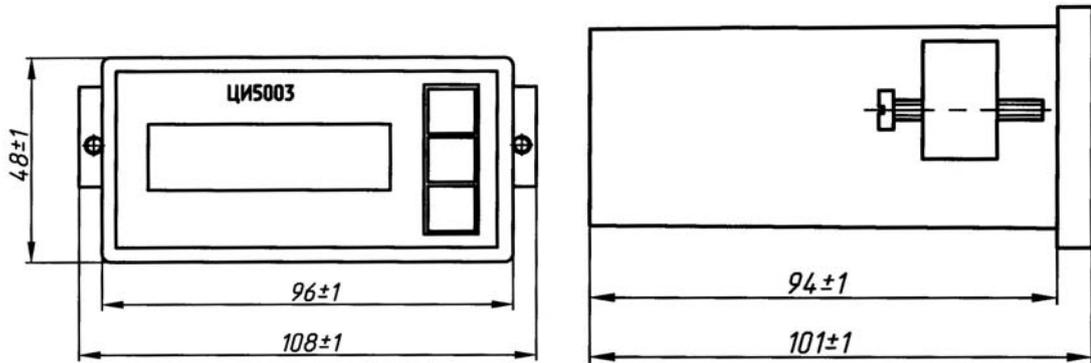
Габаритные размеры прибора ЦИ5003.
